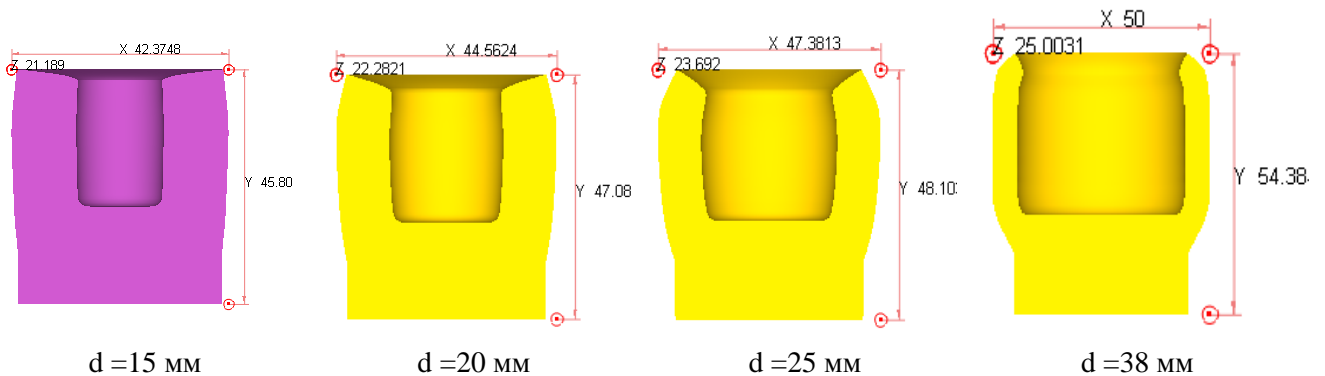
Кінцева форма виробу з розмірами, що були отримані (початкова висота розташування заготовки $h=8$ мм (див. рис. 1а))
